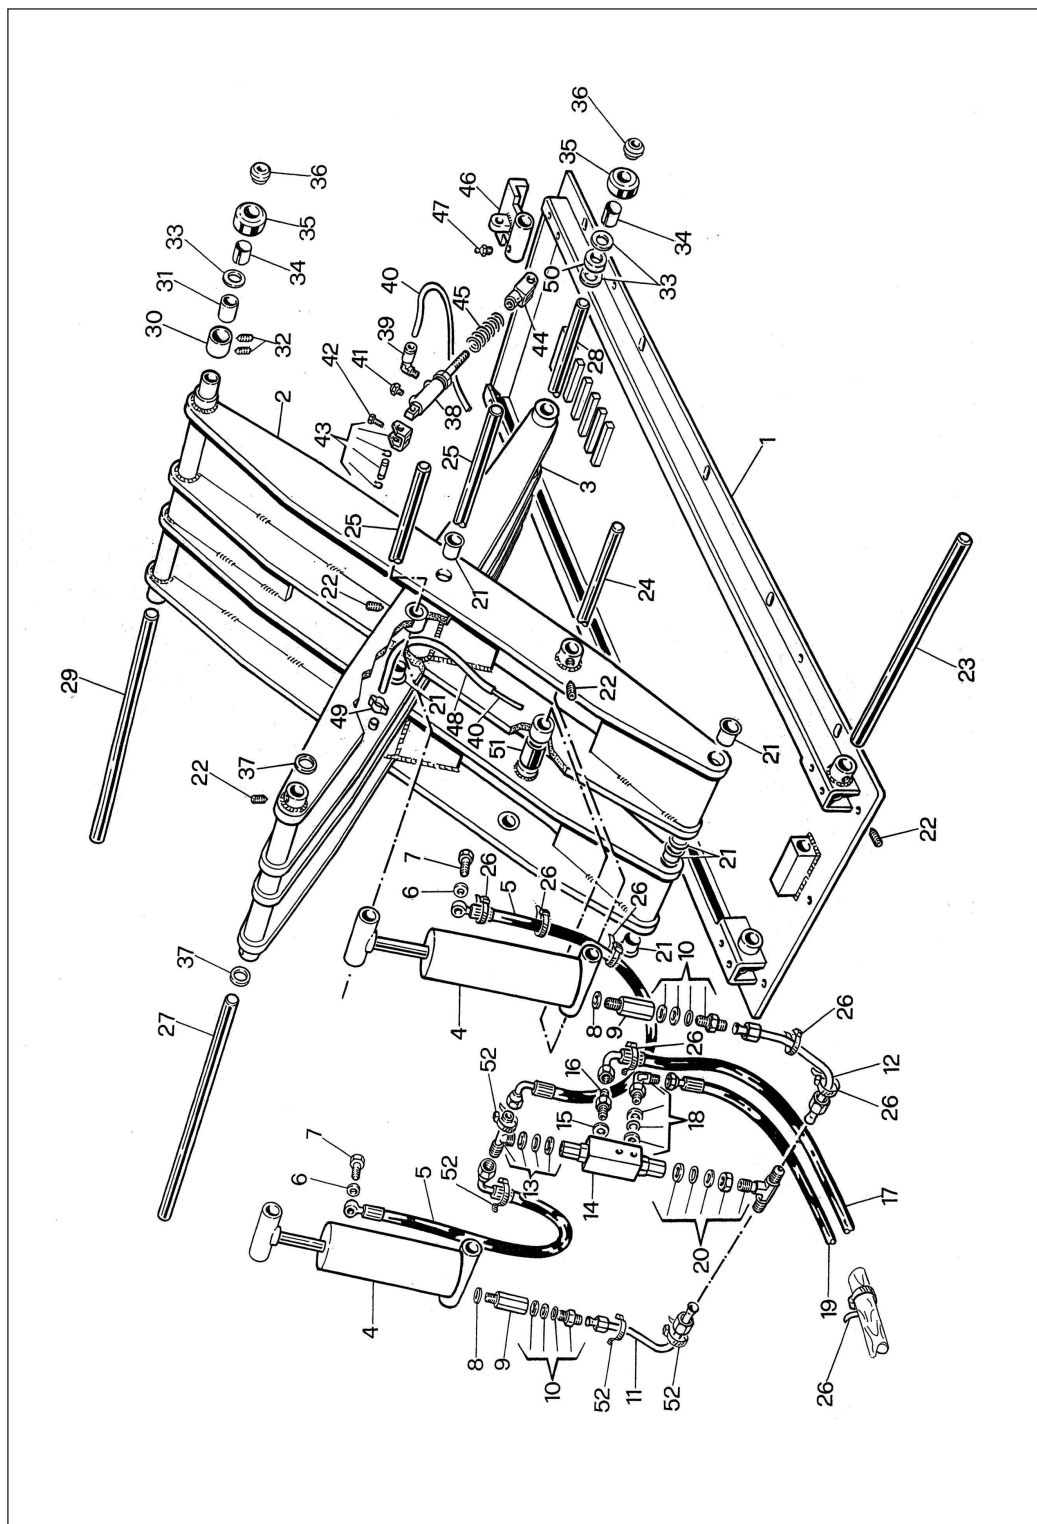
ESTRUCTURA DEL ELEVADOR
